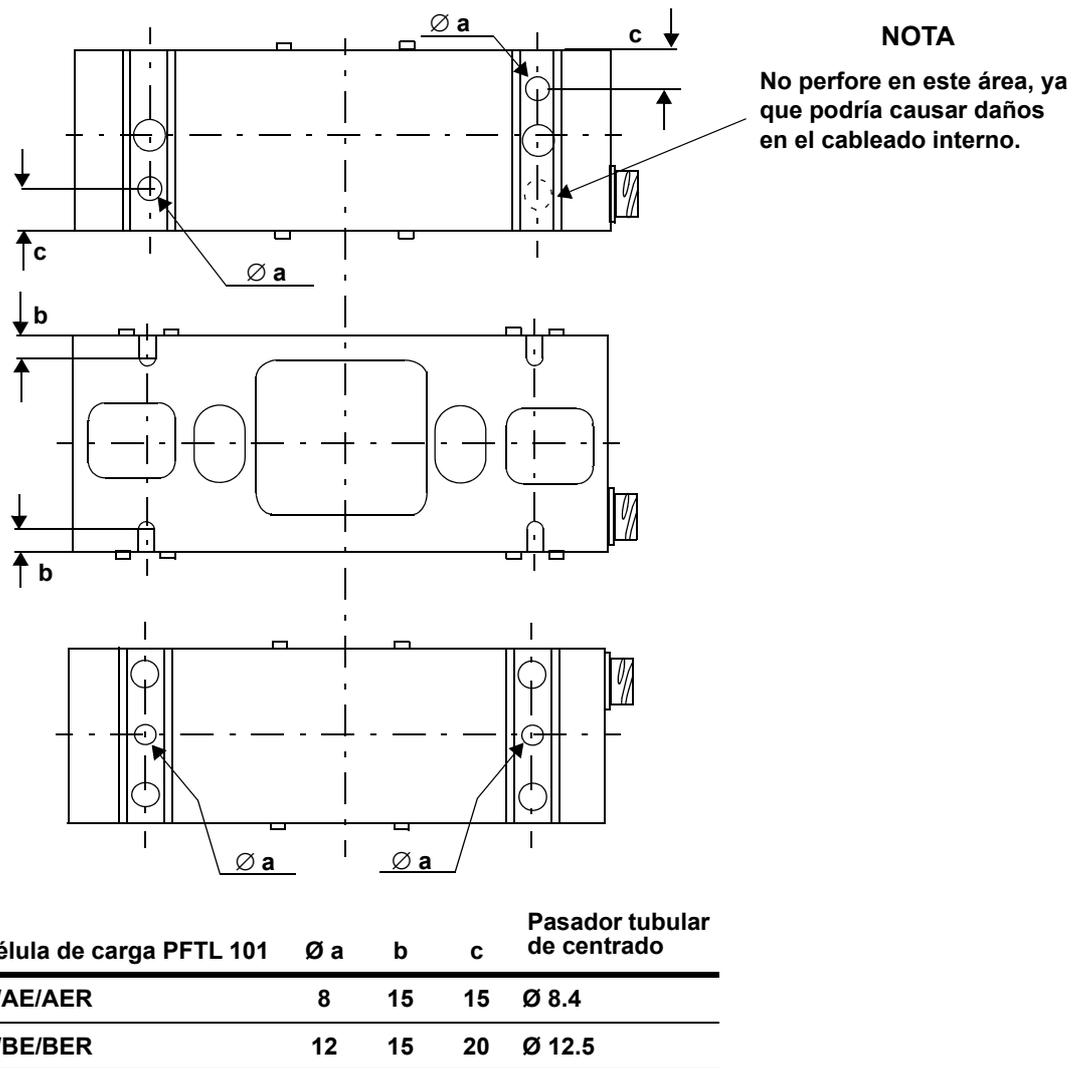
Perforación de orificios para pasadores tubulares de centrado
